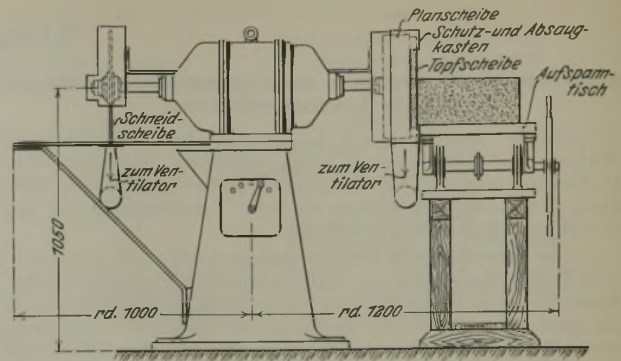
Ansicht der Stein- und Bearbeitungsmaschine.
